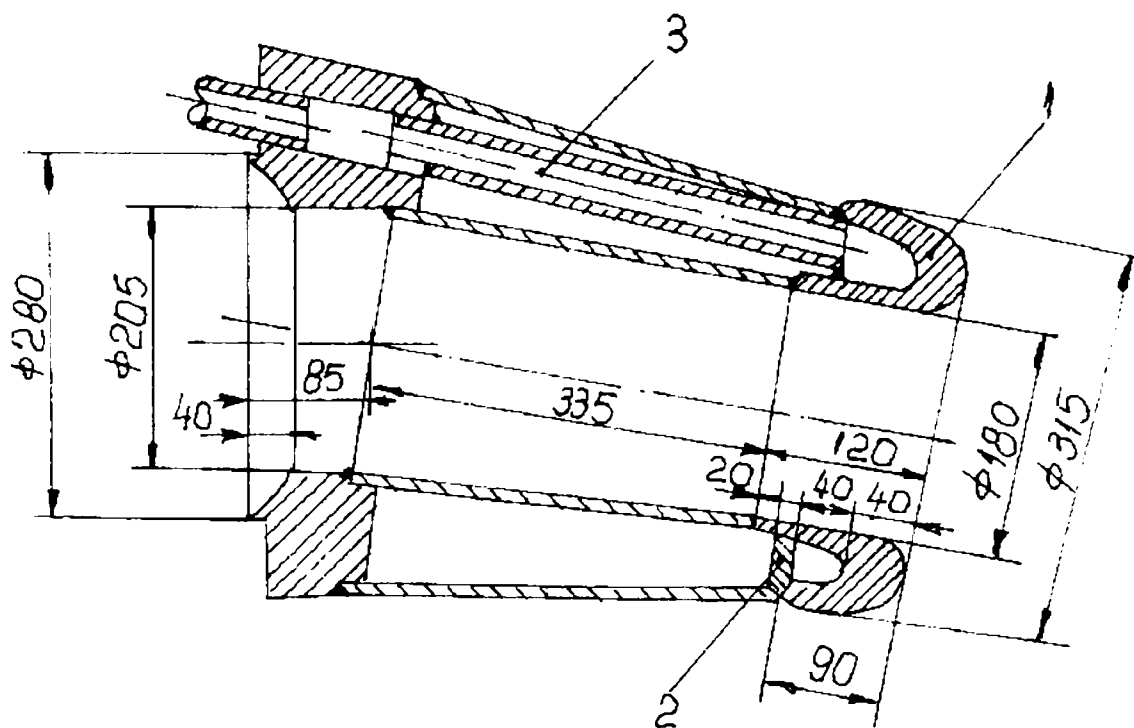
Gură de vânt de construcție Zaparoj Stali.
